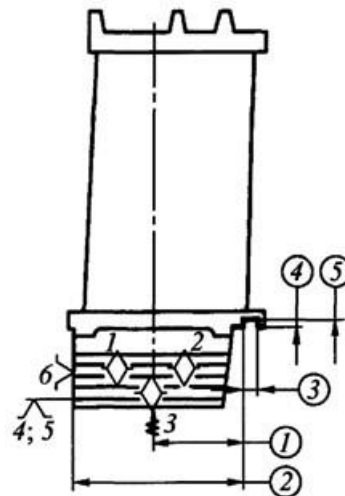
схема обробки канавки лопатки під фіксатор.
